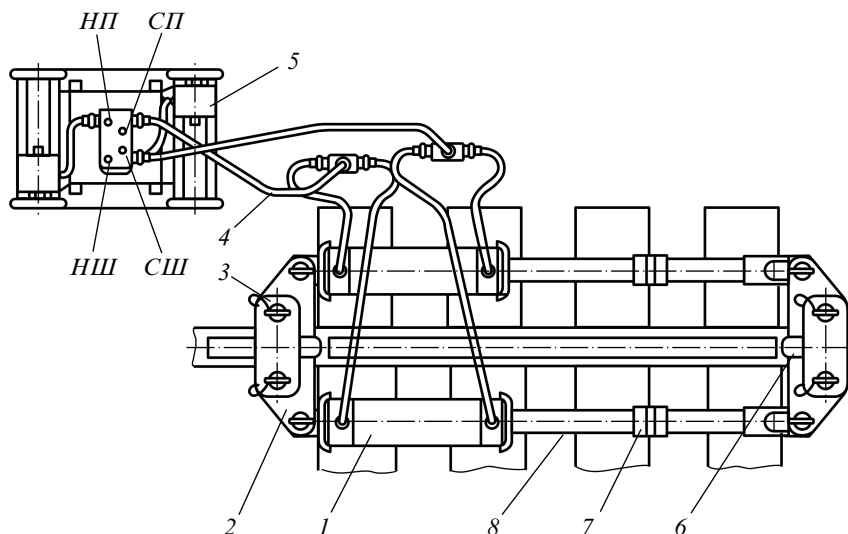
Натяжитель СПН-100-500 (вид сверху) и гидравлическая станция СГР1-8:
